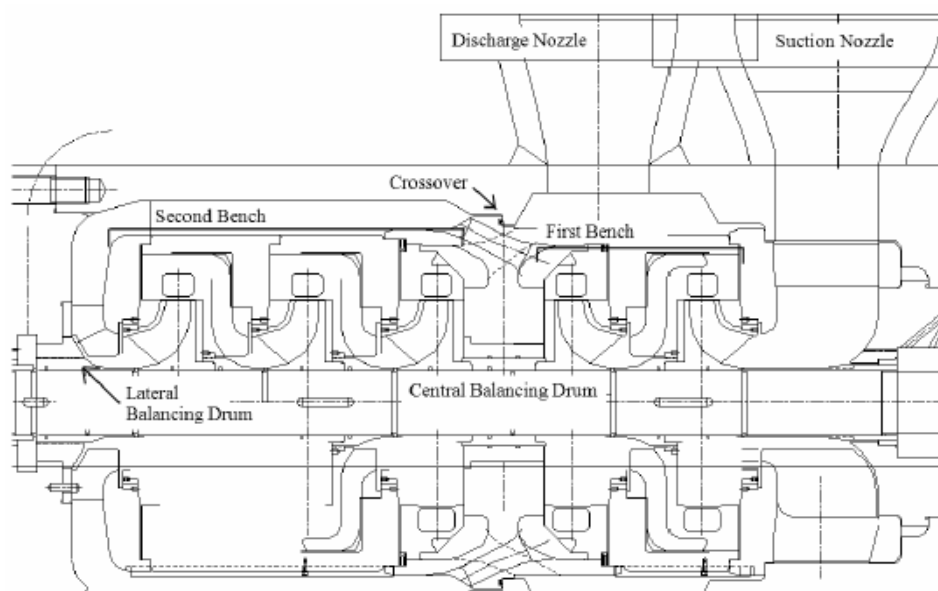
Багатоступеневий насос із зустрічним розташуванням робочих коліс, виготовлений Weir Gabbioneta
